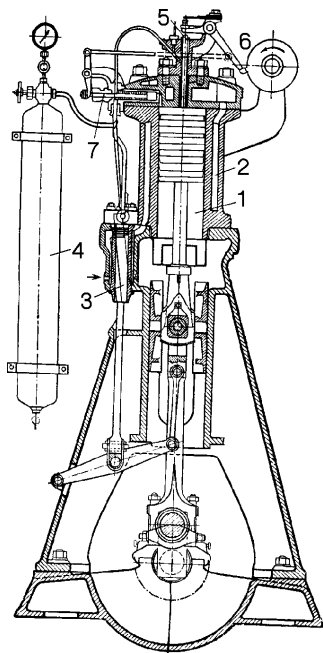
Опытный дизель: 1 — цилиндр; 2 — полость охлаждения; 3 — форсуночный компрессор; 4 — воздушный баллон; 5 — топливоподающий клапан; 6 — распределительный вал; 7 — выпускной клапан
